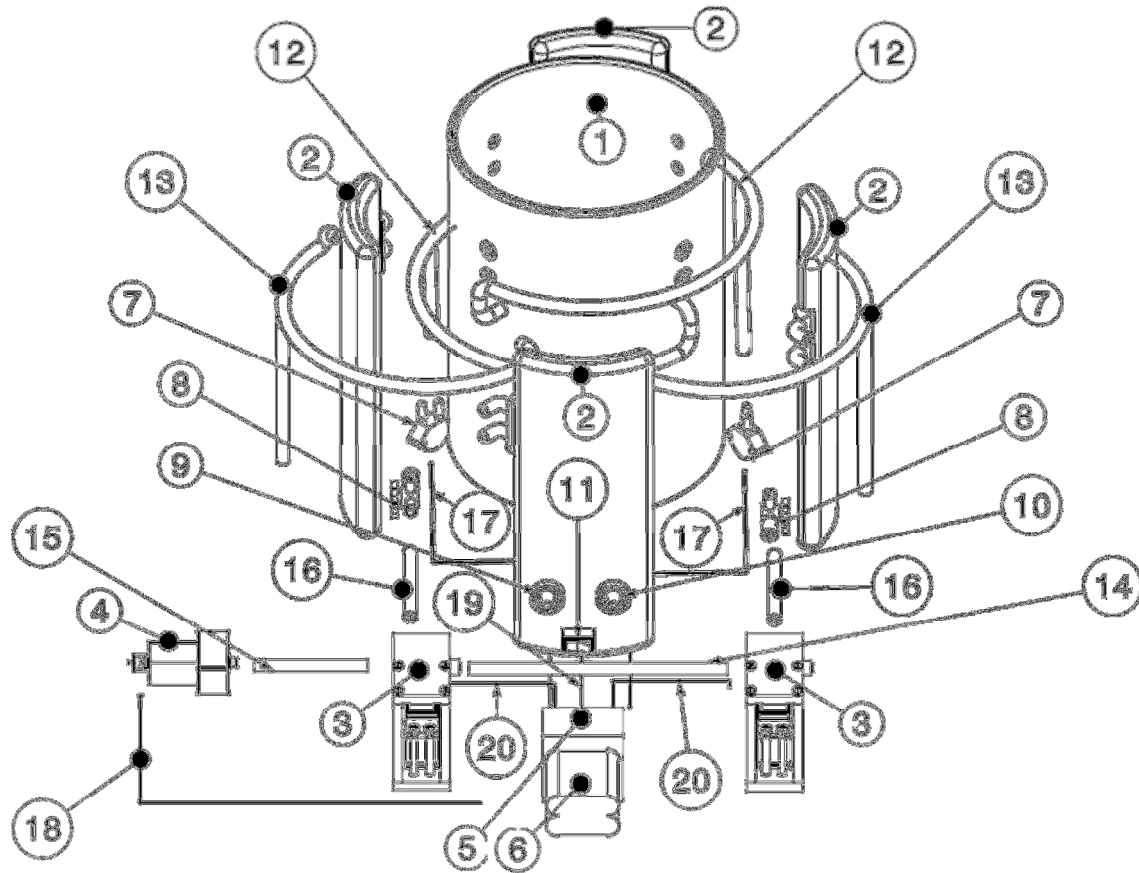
Piezas del sistema de autoajuste en explosión.
